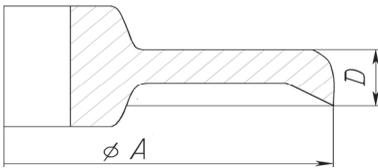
Заготовка для производства колёс и колёсных центров. (Powell-Brett)
